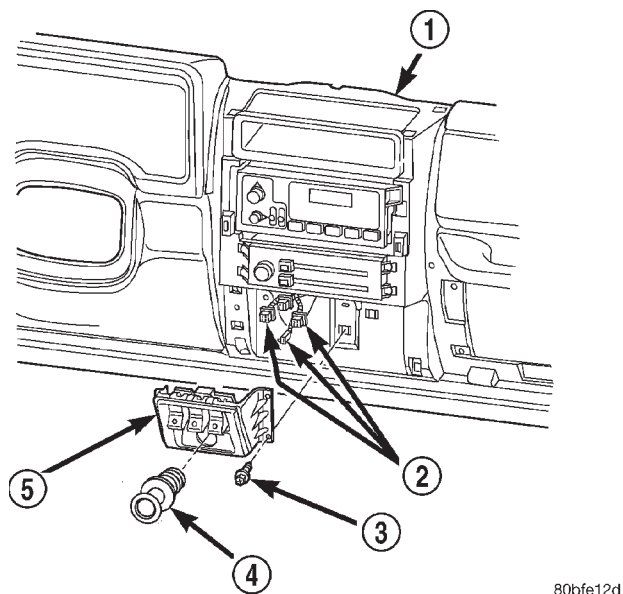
Desmontaje e instalación del marco del conmutador de accesorios
